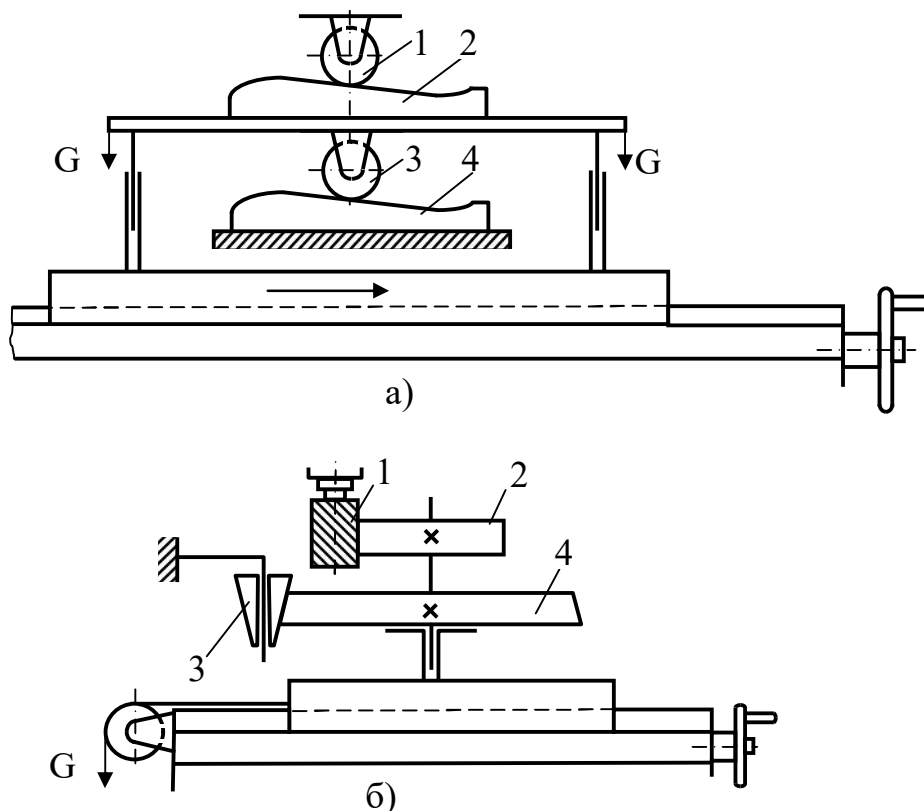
Схеми копіювального фрезерування: а – з подовжньою задавальною подачею; б – з коловою задавальною подачею; 1 – фреза; 2 – заготовка; 3 – копіювальний ролик; 4 – копір; G – вантаж
